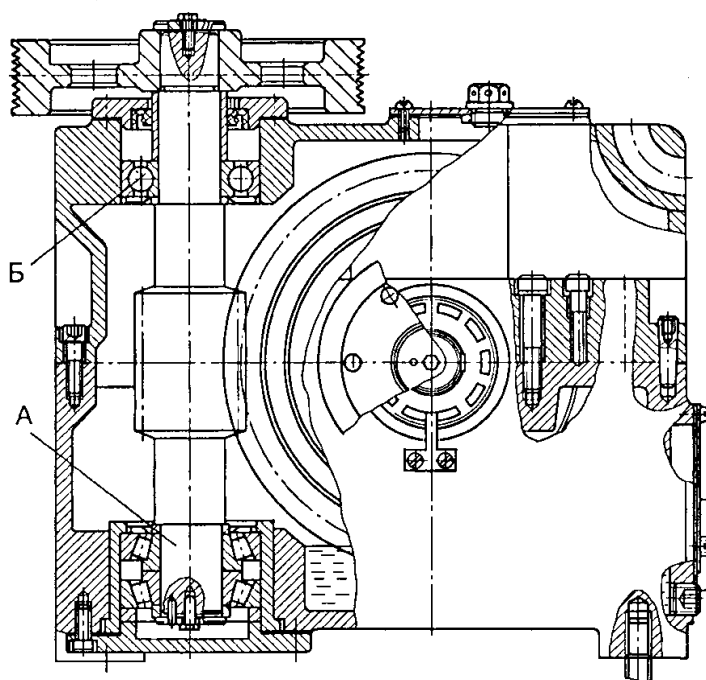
Червячный редуктор с вертикальным расположением червяка:
